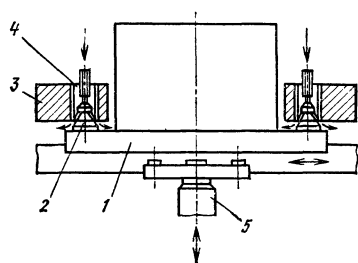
Схема пневматического контроля фиксации приспособления-спутника на рабочей позиции
